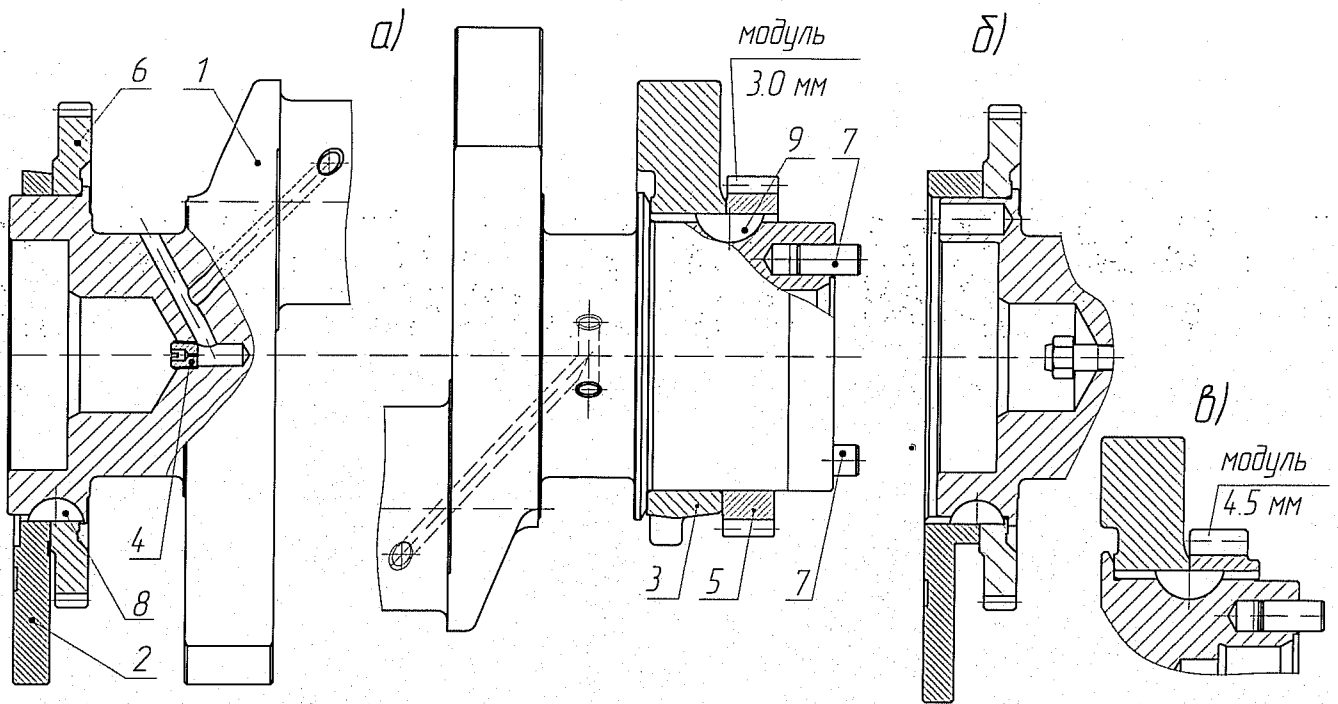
Сборочные чертежи коленчатых валов для двигателей Евро-0, Евро-1 и Евро-2, в комплектации с фланцем или гидромуфтой (а), шлицевым приводом (б), с усиленной шестерней привода ГРМ (в), собранных на базе вала 740.13-1005020.
